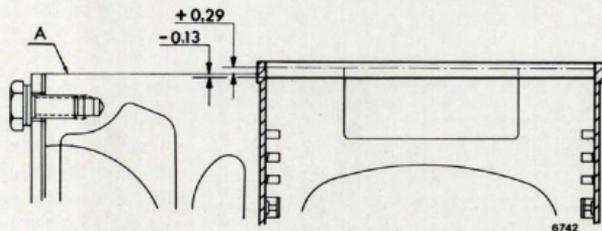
Altura de émbolos respecto a la cara del bloque
